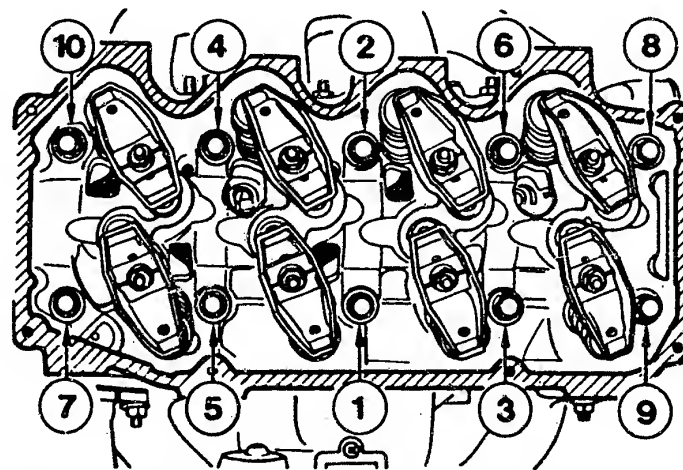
CVH-Motor: Anzugsreihenfolge der Zylinderkopfschrauben.
